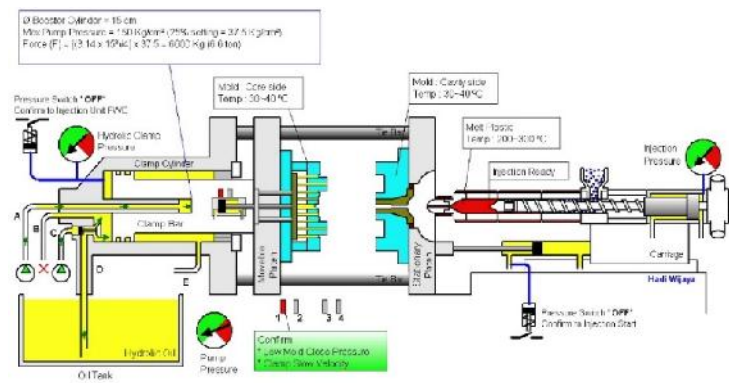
Pipa di Mesin *Injection Moulding
